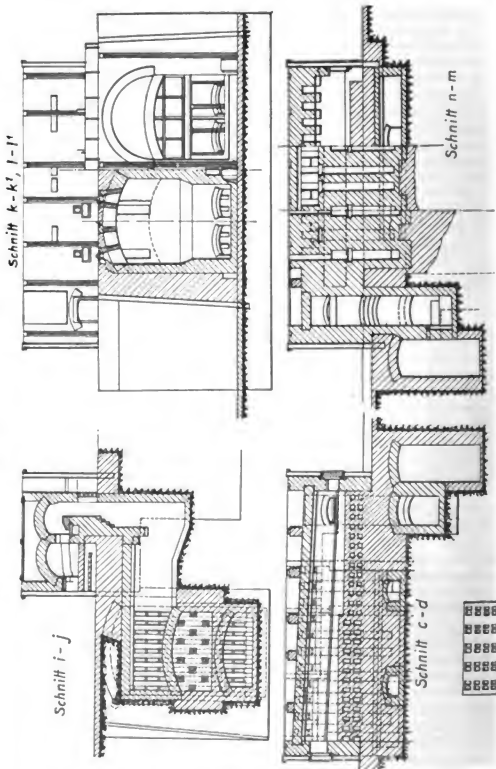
a. Rekuperator-Röhrenschweißofen.
